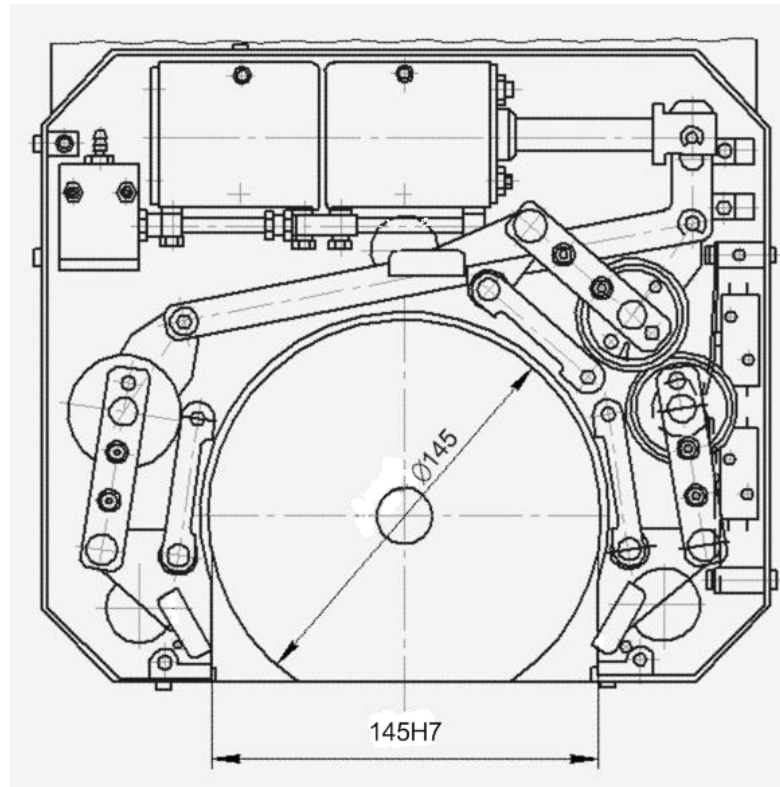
Схема нижньої плити загарбного пристрою для маніпулятора MA160П.
